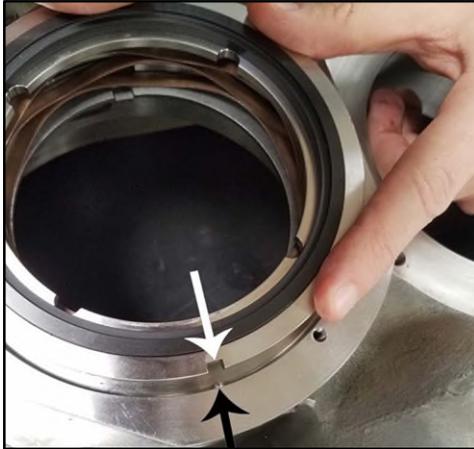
Montage des spülseitigen Dichtungsleittrings
